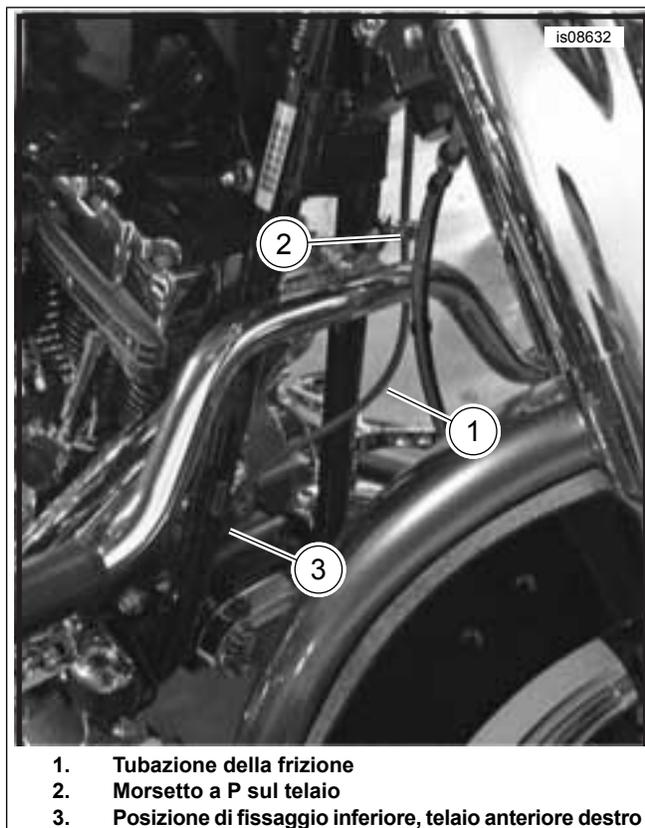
Disposizione inferiore della tubazione idraulica della frizione (modelli Softail)
